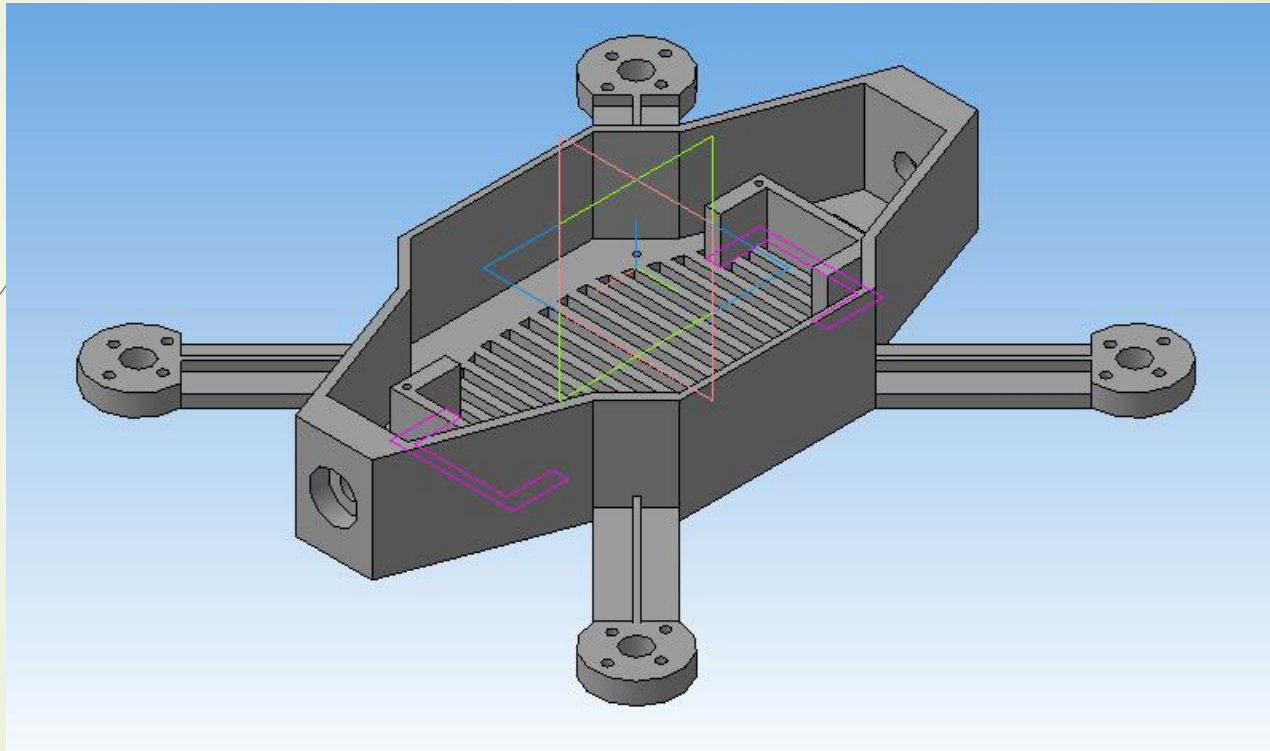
Конструкция прототипа квадрокоптера в САПР Компас-3D
